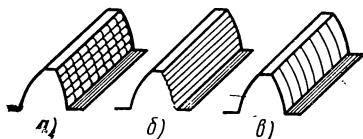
Направление резов при зубофрезеровании (а), зубодолблении (б) и зубошевинговании (в)
